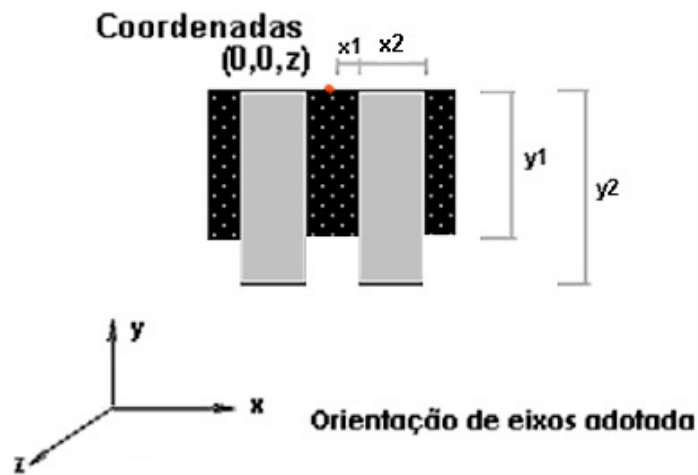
Indicação de dimensões e coordenadas adotadas durante o projeto.
